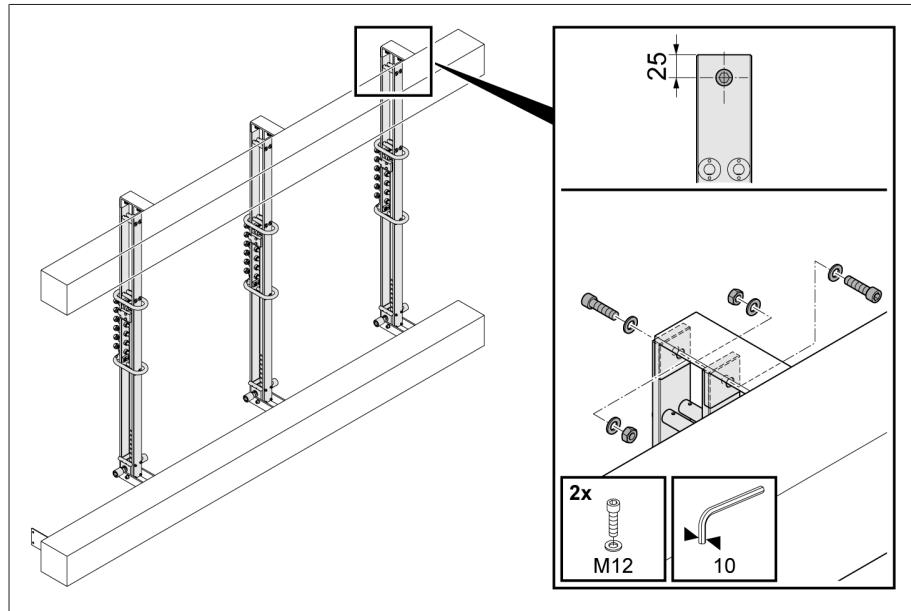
Крепление держателя, устройство ПБВ с фронтальным расположением контактов
